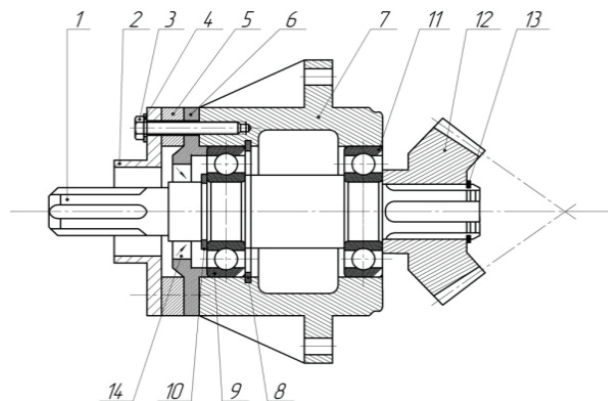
Узел привода, включающий нижеперечисленные части изделия (детали): 1 — шлицевой вал, 2 — крышка, 3 — болт, 4 — шайба, 5 — проставочное кольцо, 6 — обойма уплотнения вала, 7 — корпус, 8, 10, 13 — стопорные кольца, 9 и 11 — шариковые подшипники, 12 — коническое зубчатое колесо, 14 — кольцо уплотнения вала
